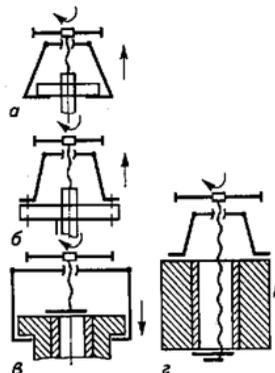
Схема применения съемников: а – с лапками для захвата детали при выпрессовке; б – с лапками, закрепленными на детали для выпрессовки; в – для выталкивания детали; г – для вытаскивания детали
